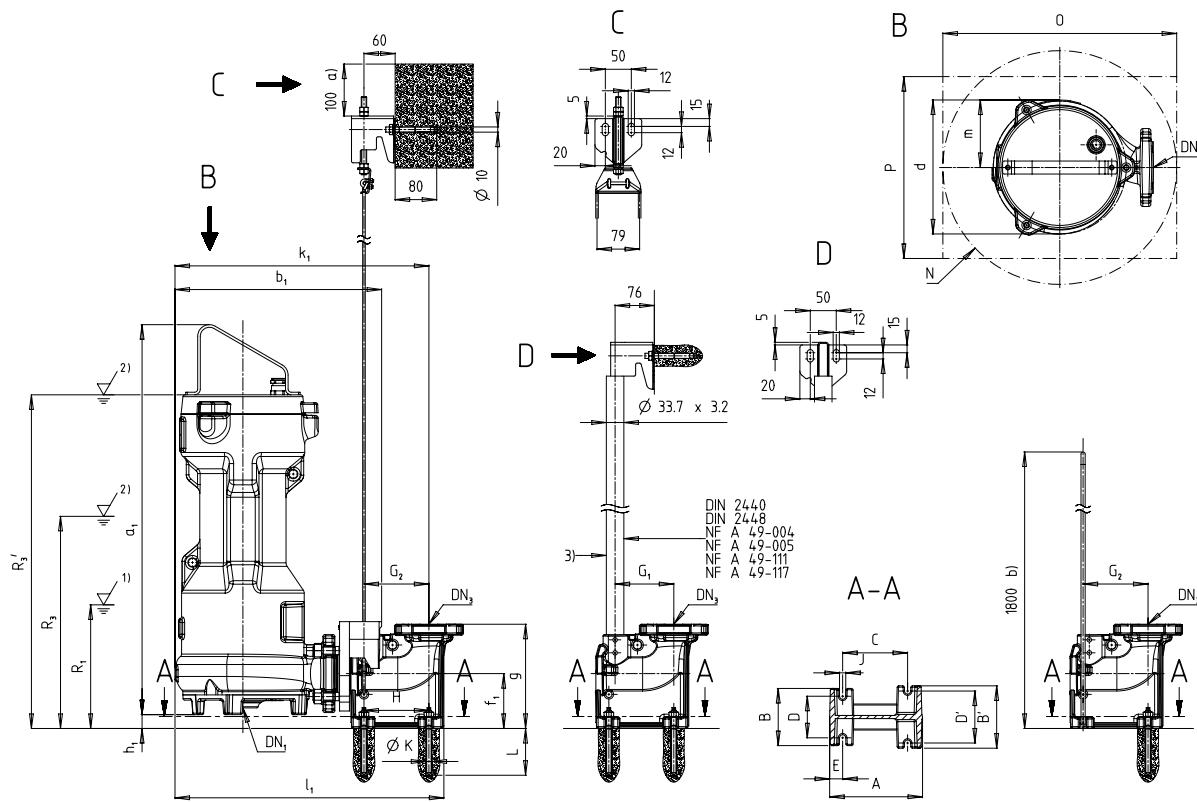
Dimensões, instalação fixa, guiamento por cabo, guiamento de 1 barra, guiamento por grampo
